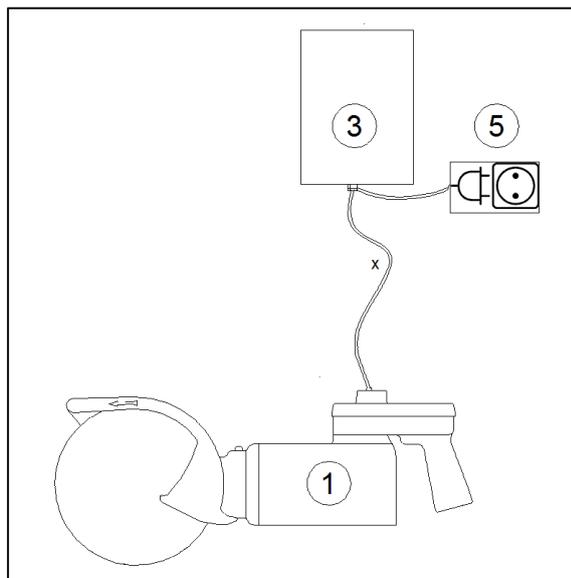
Anschlussleitungen für Maschinen mit Motor 03/13/03L und Motor 06/06L
